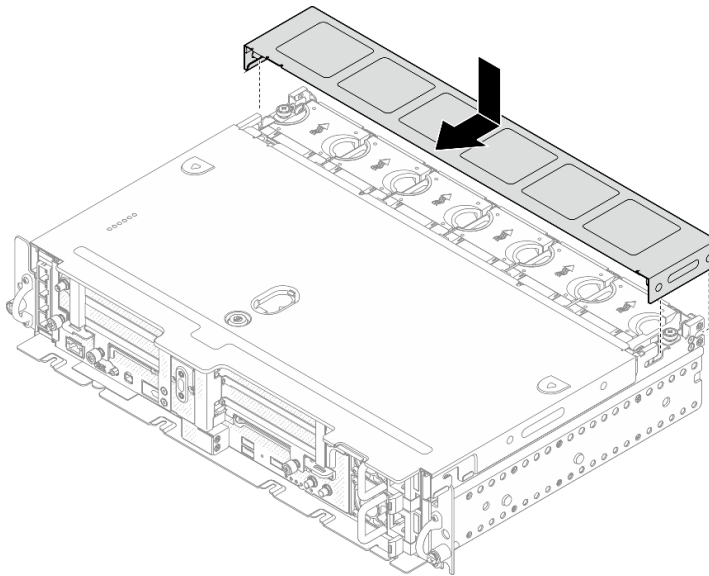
Instalación de la cubierta del ventilador (300 mm)
